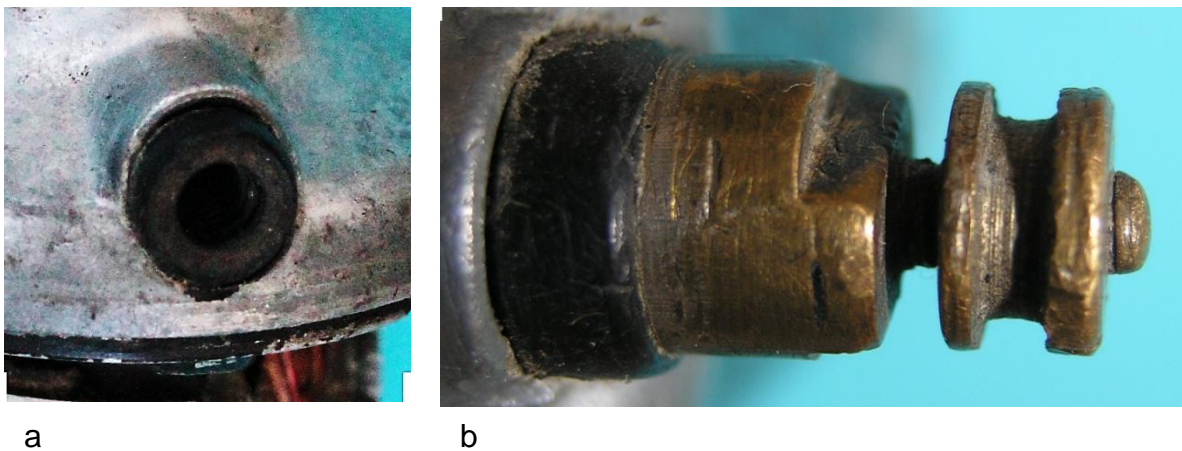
Kabelanschlussbolzen in der isolierten Bohrung des Lagerhalses eingeschraubt
